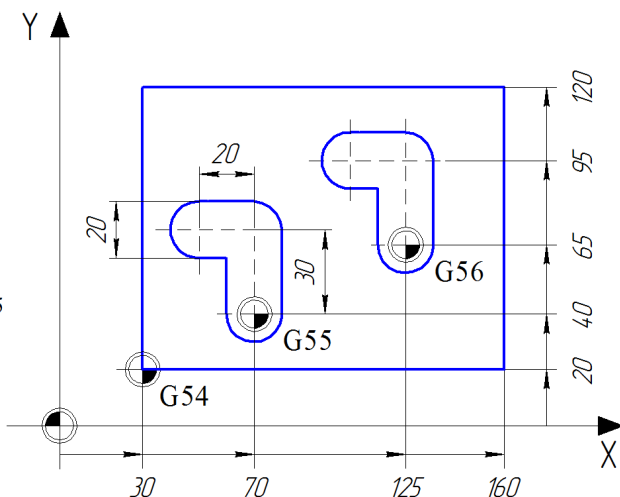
Смещение нулевой точки заготовки в места врезания фрезы при формообразовании пазов
